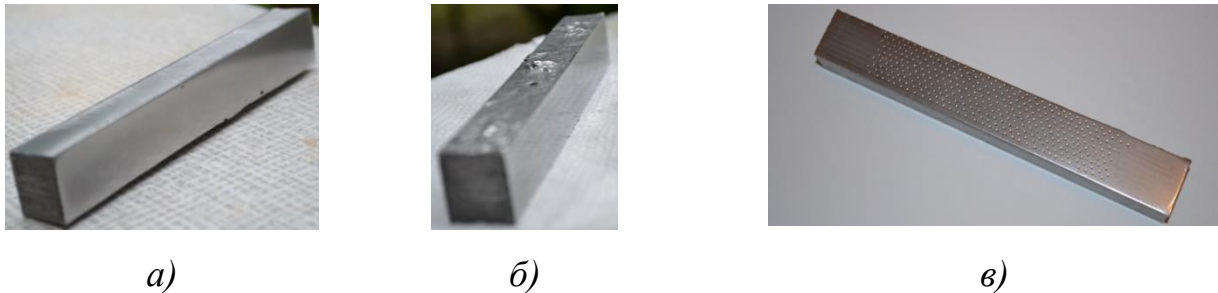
Заготовка – зразок: розташування вверху *а)* базовою поверхнею; *б)* вхідною литою поверхнею; *в)* після вимірювань твердості
